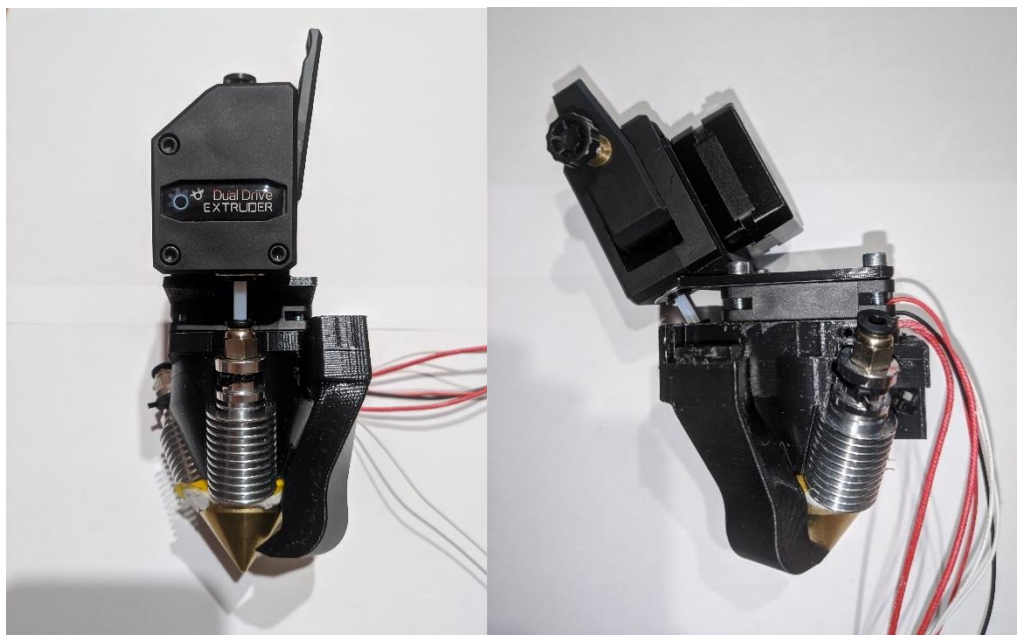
Montagem do motor e da extrusora *direct drive*.
